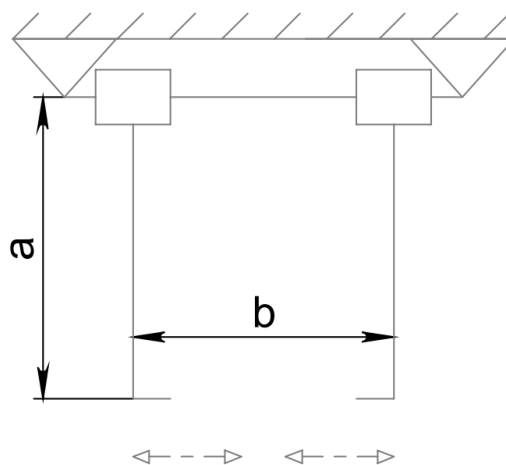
Кинематическая схема захвата с поступательным движением губок схвата
